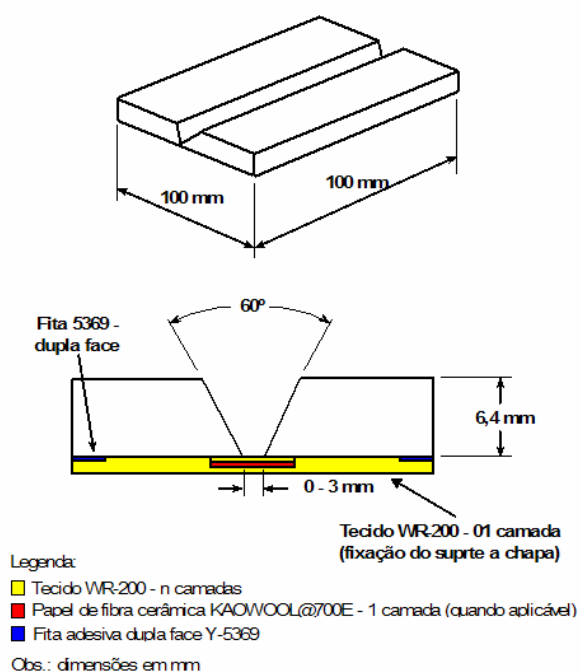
Desenho esquemático com dimensões do chanfro e montagem do suporte na chapa
